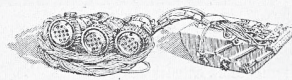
Экспериментальный щуп для контроля сварных соединений методом «бегающего луча».
